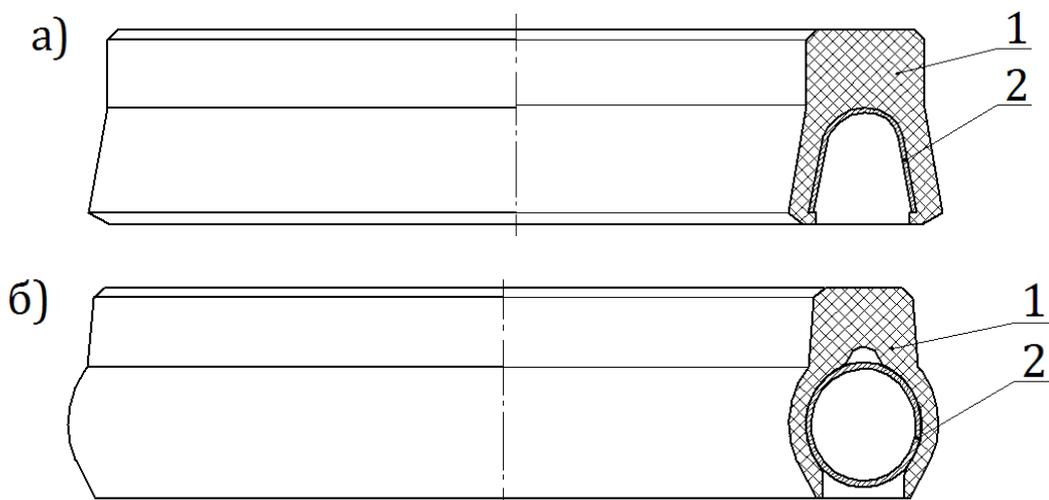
Внешний вид манжеты: а – с пластинчатой пружиной,
